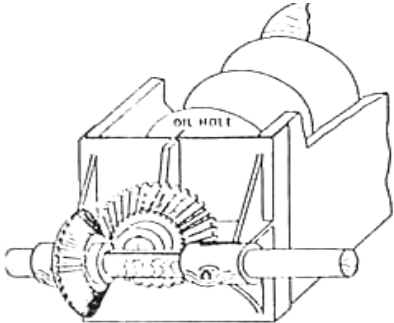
menunjukkan beberapa tipe hanger. Gbr 2.9-a menunjukkan tipe paling sederhana dan paling murah. Gbr 2.9-b menunjukkan tipe yang mempunyai persambungan terpisah dan ditempatkan di wadah baja. Bentuk yang lebih rumit mempunyai persambungan yang dapat disetel dan juga dengan cara meminyaki yang lebih baik.
